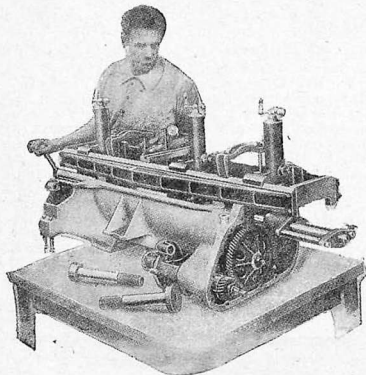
Работа приспособления установленного на картере мотора при расточке коренных подшипников
